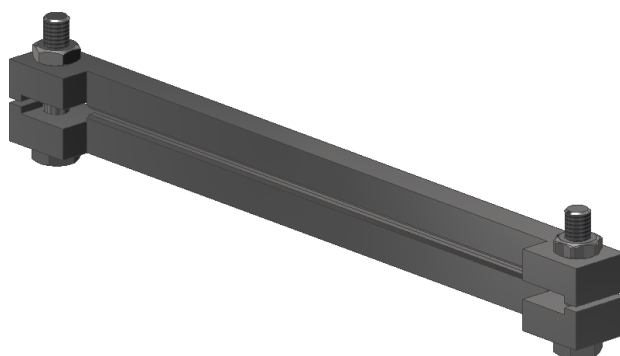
Параметрическая 3D модель прижима для сварки пластин в конверт
